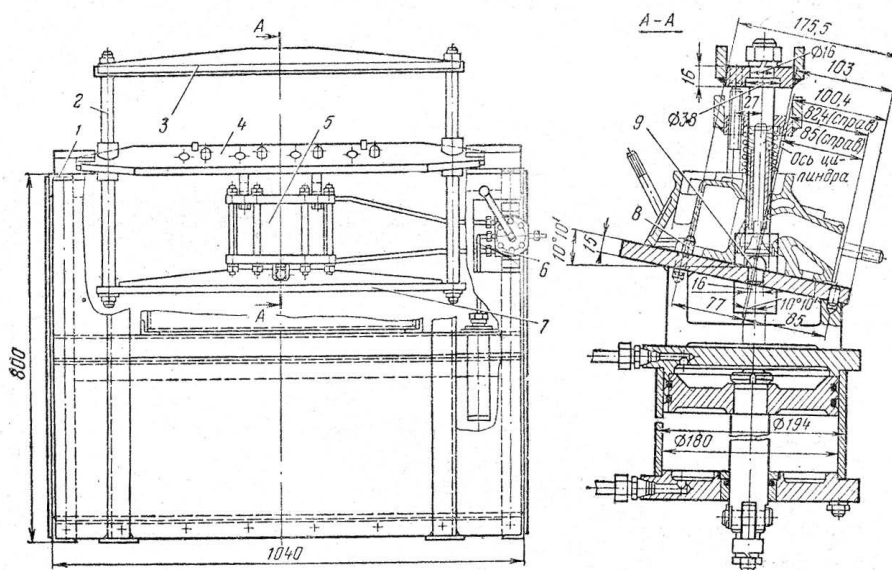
Стенд для розбирання головки циліндрів, модель TP-6703
